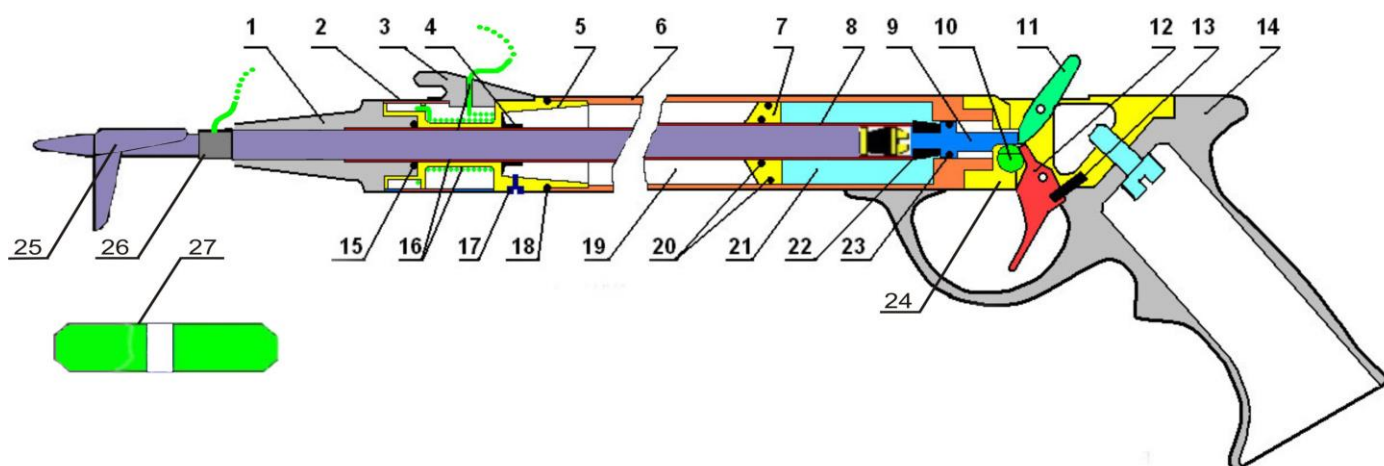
1-конус, 2-крышка катушки, 3-зацеп, 4- воздушный клапан, 5- катушка, 6-ресивер, 7-поршень, 8- рабочий гидроцилиндр, 9- гидроклапан, 10- регулятор-предохранитель, 11-линьсбрасыватель, 12-спица, 13- пружина спицы, 14- рукоятка, 15-уплотнение, 16-линь, 17-винт стравливания воздуха, 18-уплотнение, 19- сжатый воздух, 20-уплотнение поршня, 21-вода, 22-манжета, 23-уплотнение, 24- корпус, 25- гарпун, 26-скользящая втулка, 27-накладка для взведения.
